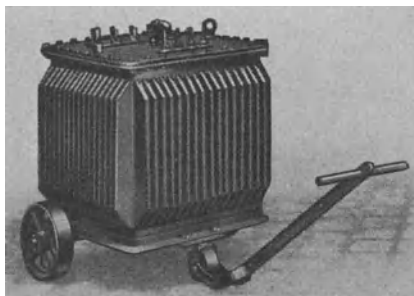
Fahrbarer Schweißumspanner mit Ölkühlung.
